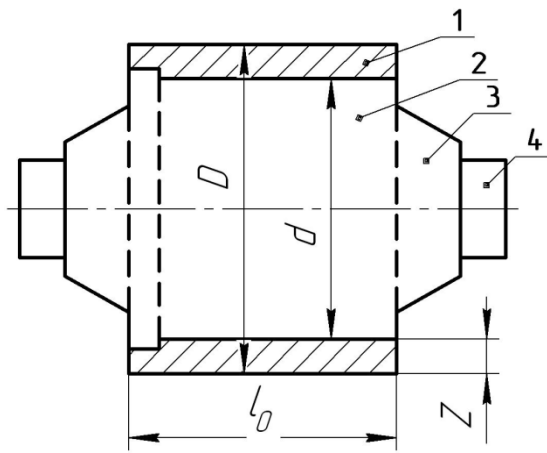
Складений опорний валок стана холодної прокатки штаб: 1 – бандаж; 2 – вісь; 3 – шийка; 4 – хвостовик
